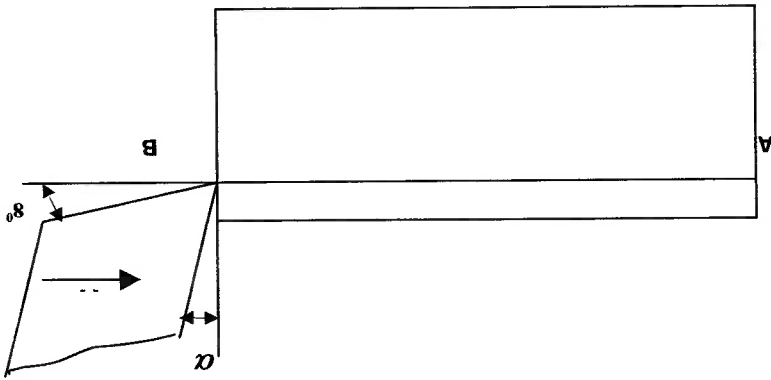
Modelo físico do processo de usinagem ortogonal
